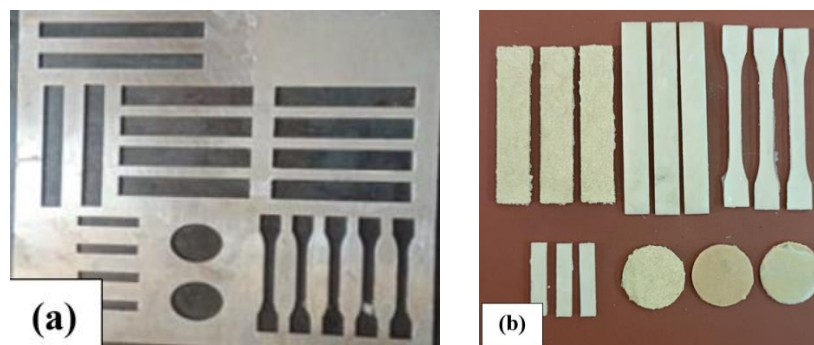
(a) Moule ; (b) Eprouvettes élaborées.
